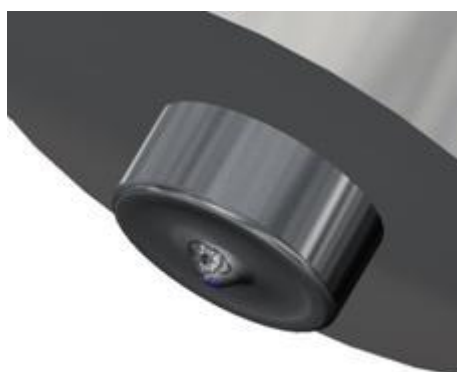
Инструмент из кубического нитрида бора для перемешивающей сварки трением встык тонких стальных листов.
